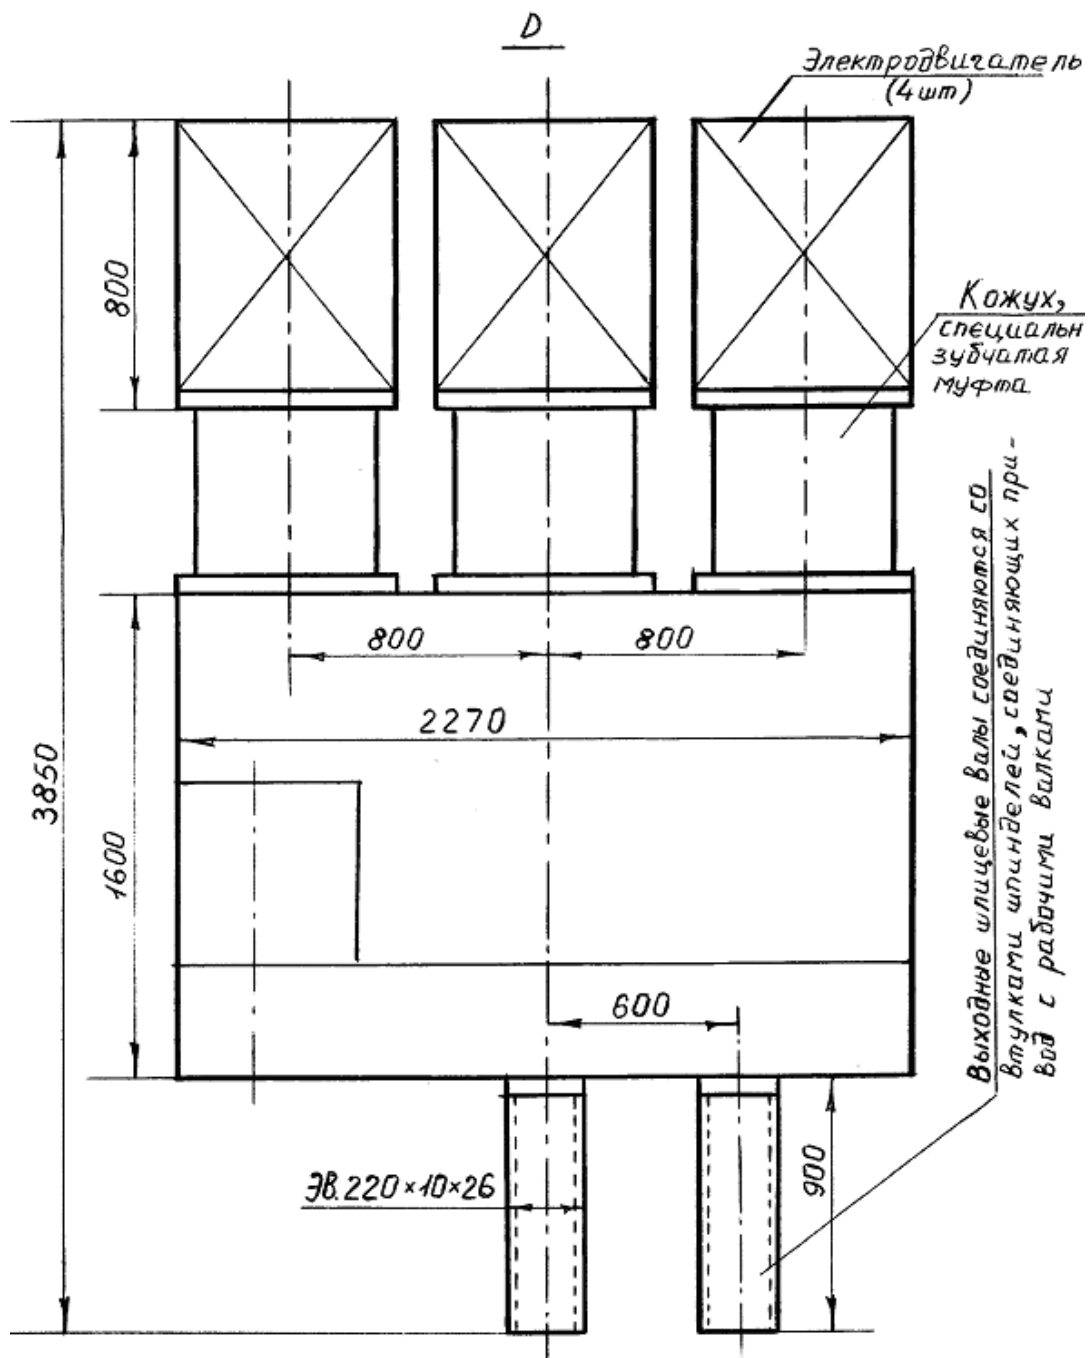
Привод вертикальной клетки прокатного стана. Сборка шестерённой клетки, редуктора и электродвигателей
